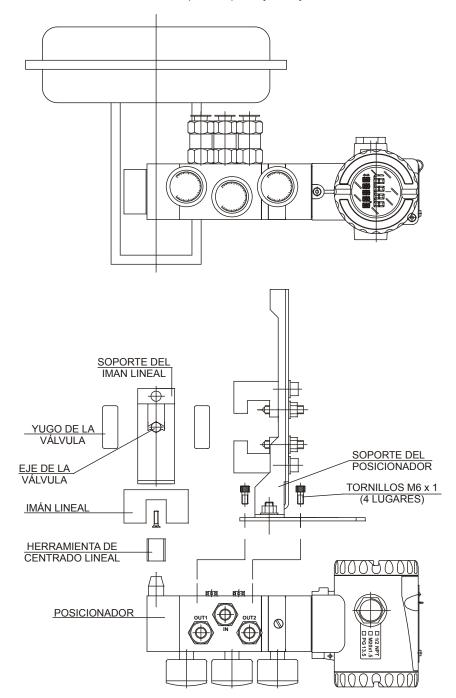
Esquema de montaje del Posicionador en un Actuador Lineal
